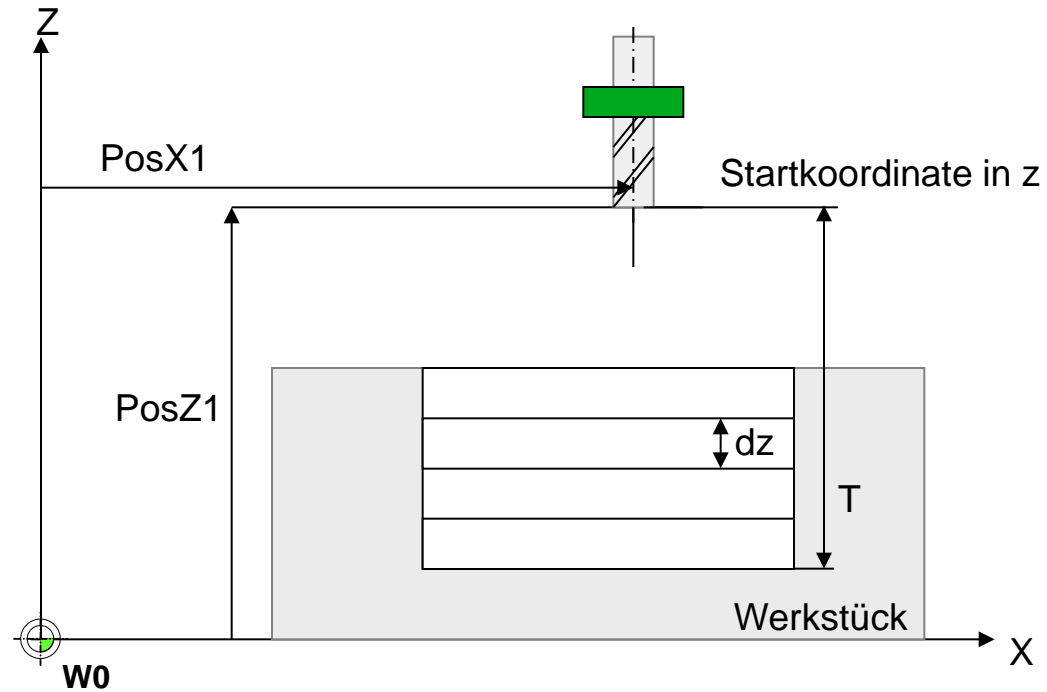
Parameter für die Definition einer rechteckigen Frästasche
